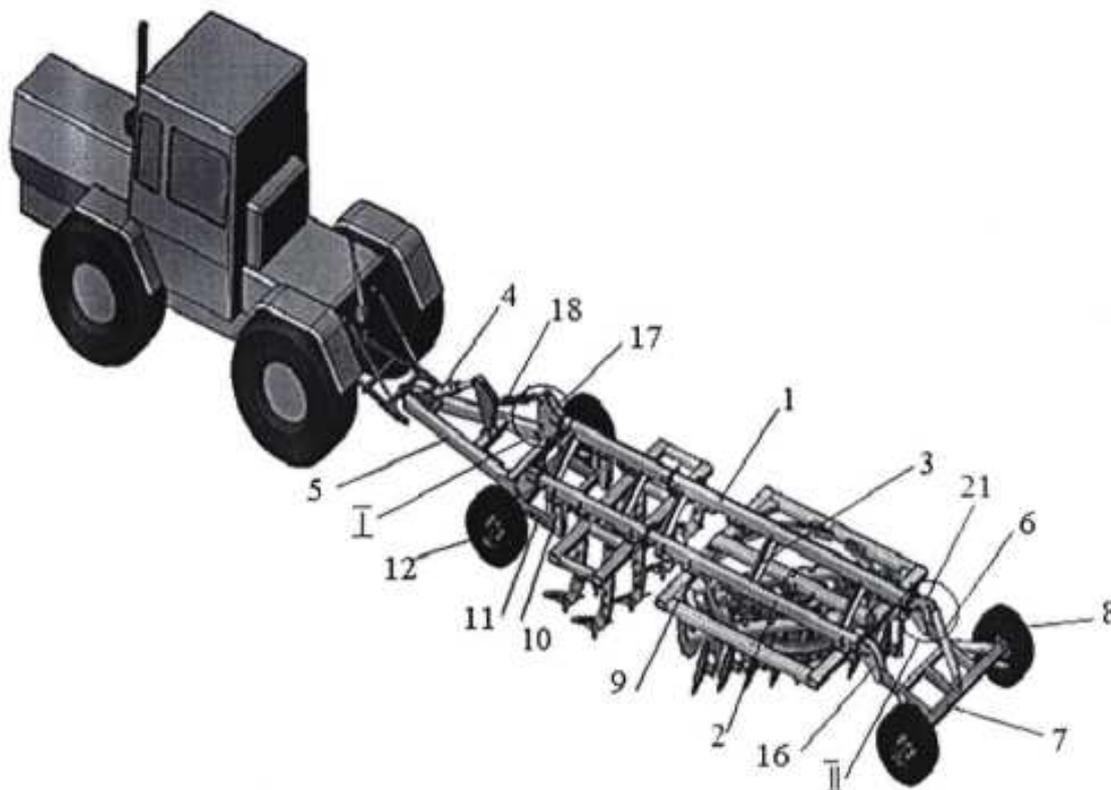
Схема агрегата почвообрабатывающего универсального
